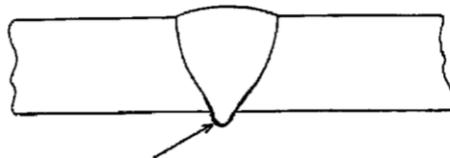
Aspecto del exceso de penetración en la soldadura
